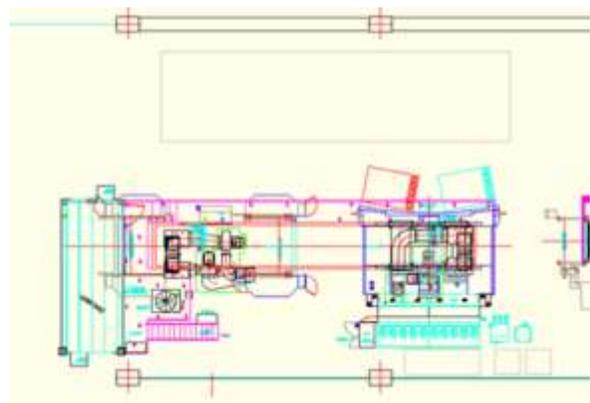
Segnalazione a layout anche delle aree di stazionamento ponte e serbatoi gruppo lavaggio e inchiostrazione.
